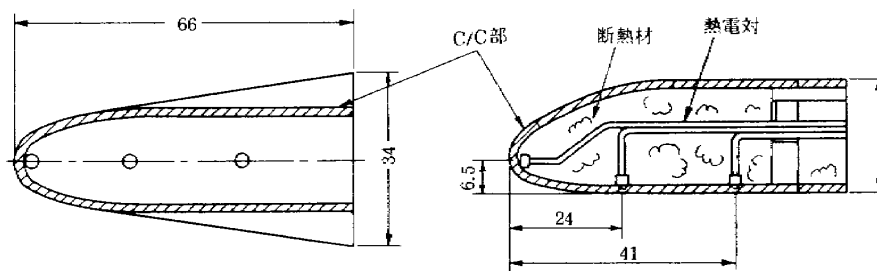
検証モデル構造及び熱電対配置図(単位: mm)
